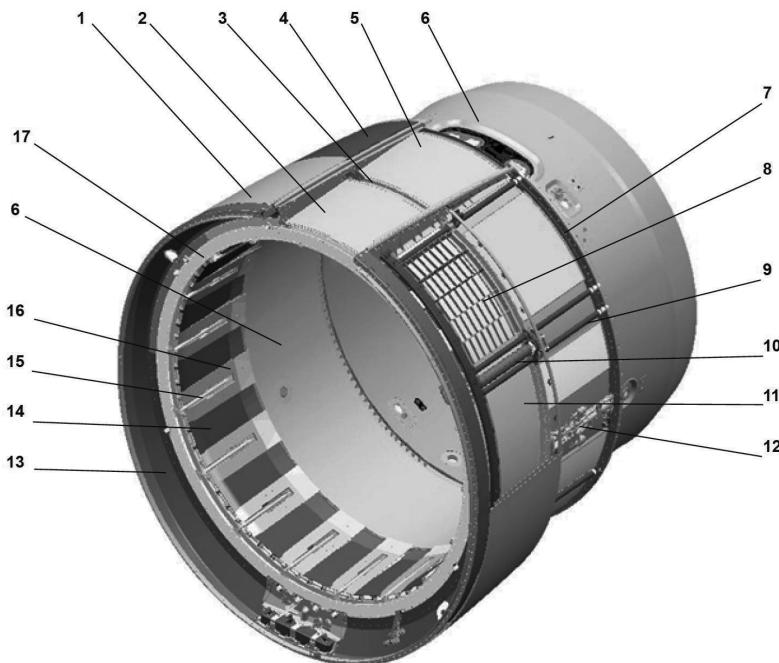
Основные элементы конструкции реверсивного устройства двигателя ПС-90А:
